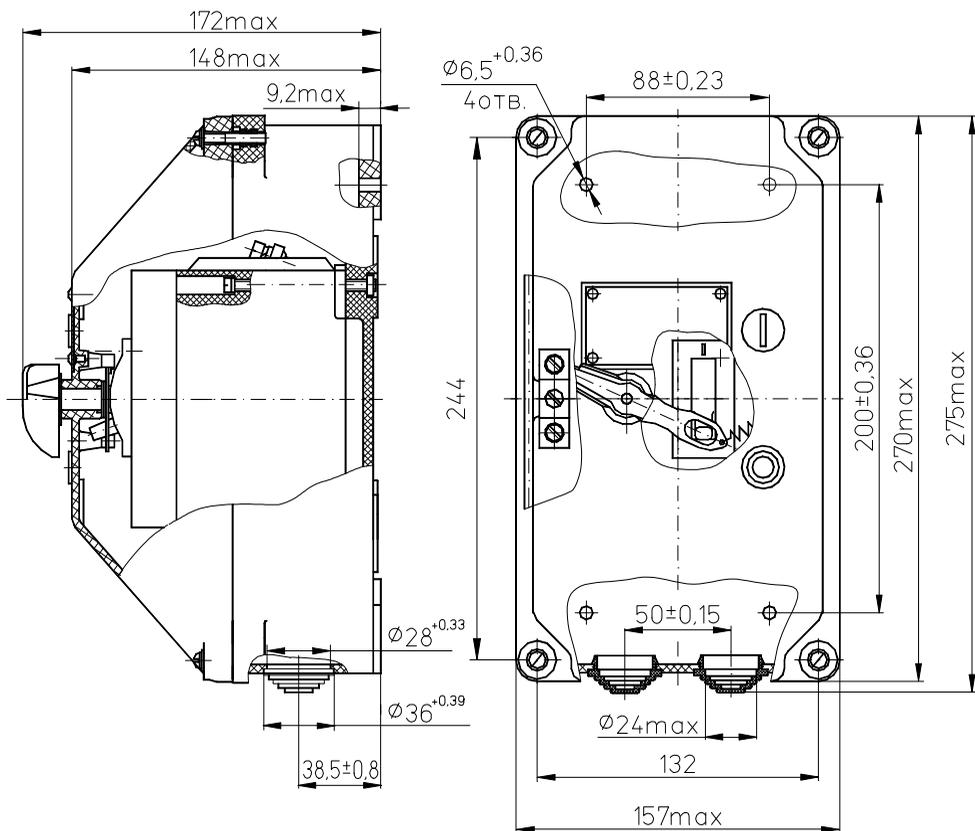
Выключатель в дополнительной оболочке с кабельными вводами (двух- и трехполюсный)
